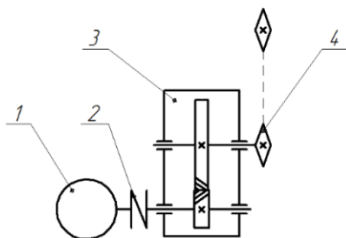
Схема привода: 1 – электродвигатель; 2 – муфта; 3 – закрытая цилиндрическая косозубая передача; 4 – цепная передача
